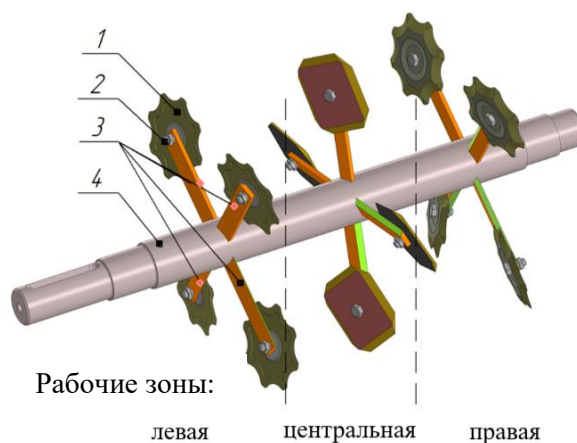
Схема размещения образцов: 1 – испытываемые режущие элементы; 2 – болтовое соединение; 3 – держатель; 4 – вал
